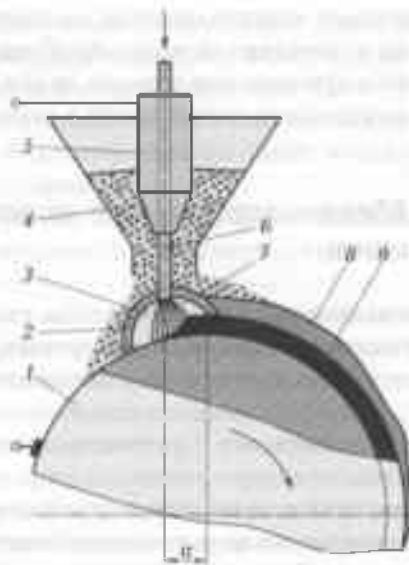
Автоматическая сварка и наплавка под слоем флюса:
